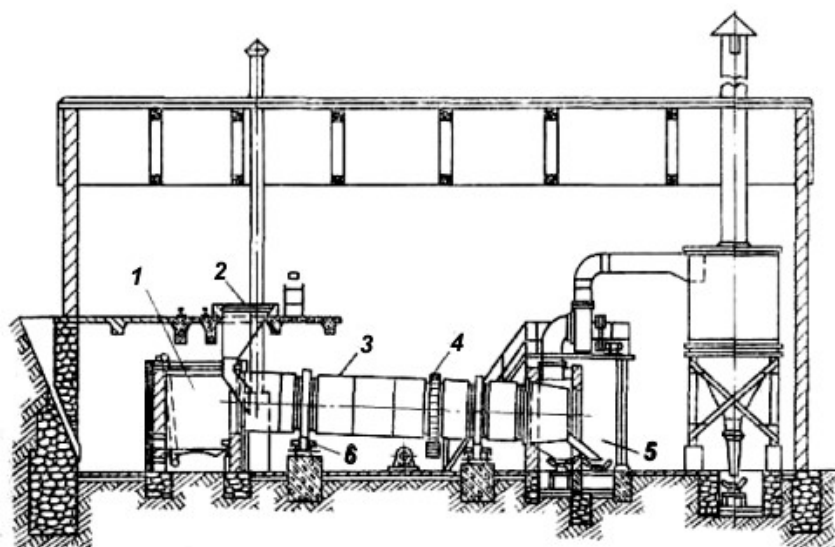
Барабанное сушило: 1 – топочная камера; 2 – загрузочный бункер; 3 – барабан; 4 – ведущая шестерня; 5 – выгрузка сухого материала; 6 – роликовые опоры
